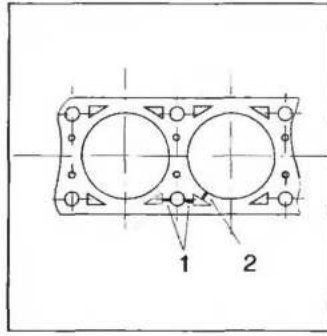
Трещины на верхней плоскости блока: 1 — между резьбовым отверстием и рубашкой охлаждения; 2 — между цилиндром и рубашкой
